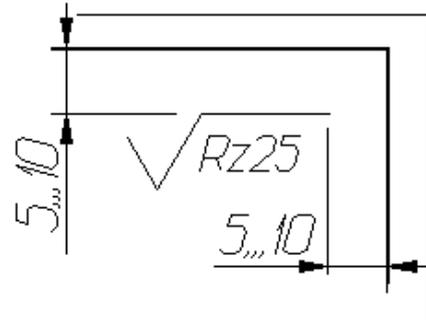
Указание шероховатости одинаковой для всех поверхностей изделия
